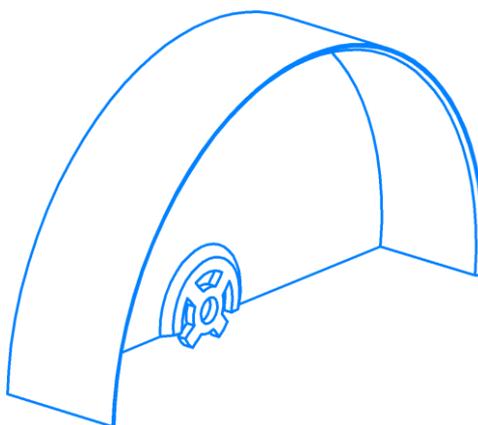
Внешний вид приспособлений для малого и большого зеркал.
